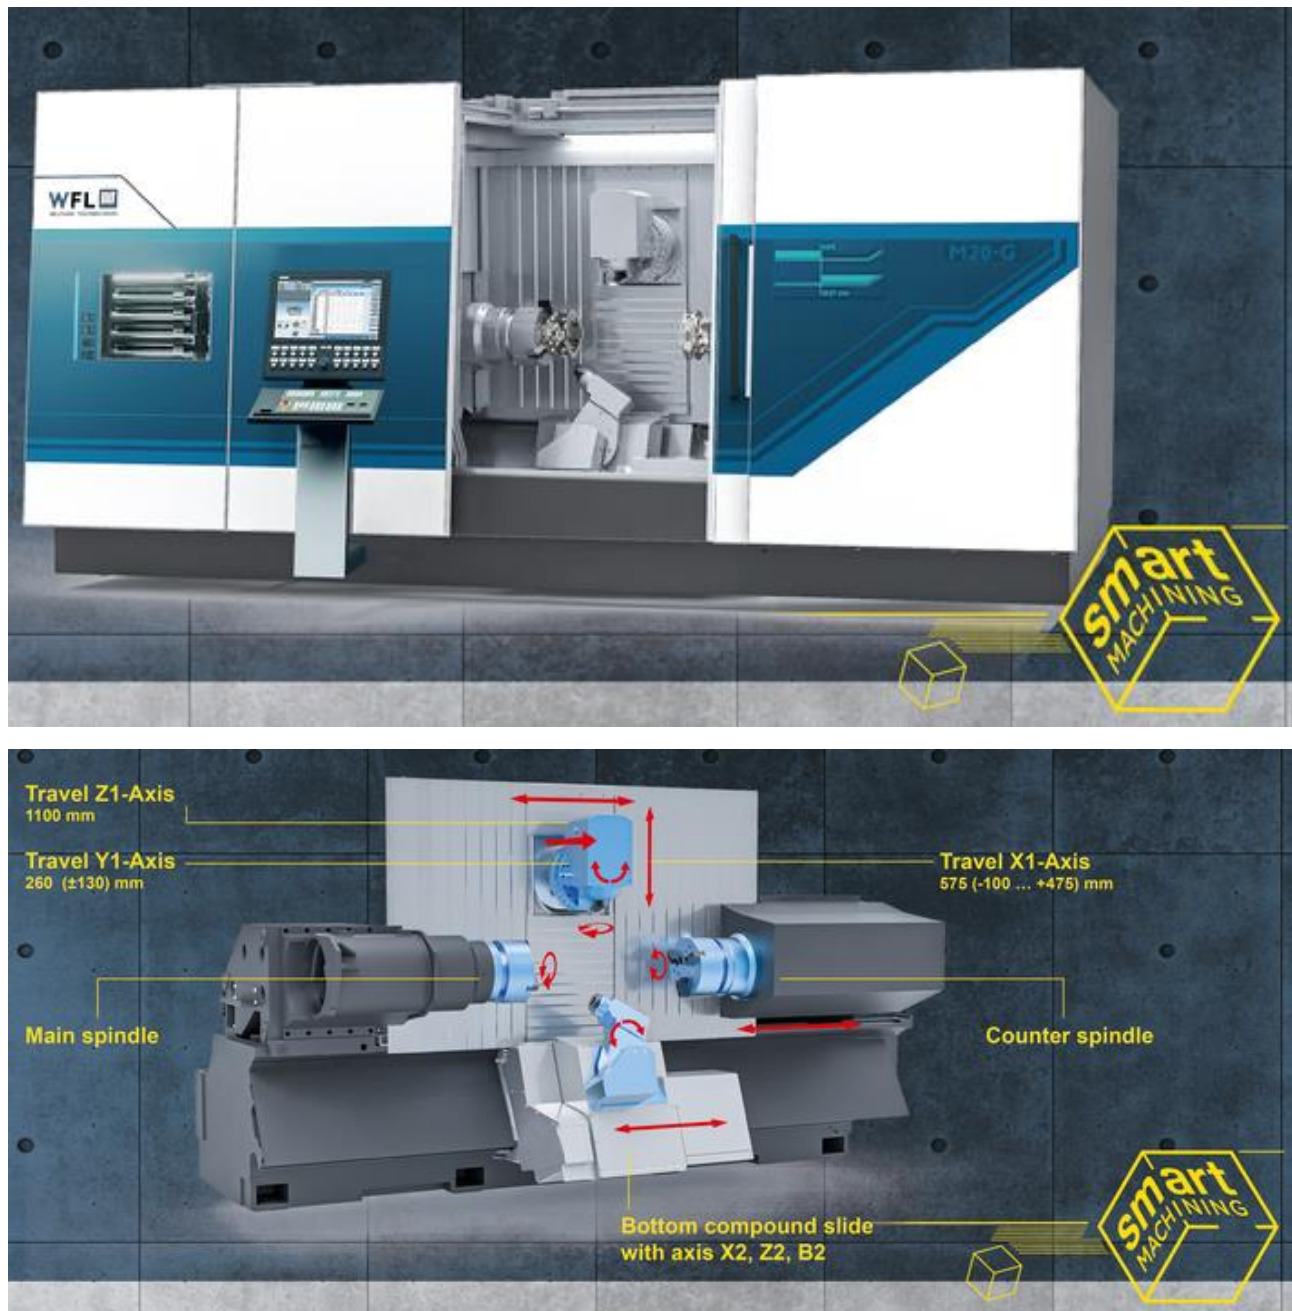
Токарно-фрезерний обробний центр MILLTURN WFL.
